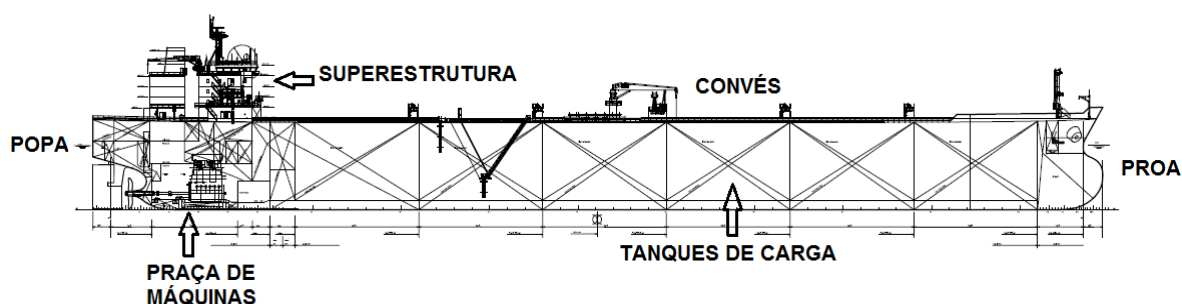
Ilustração da vista longitudinal de um arranjo geral
